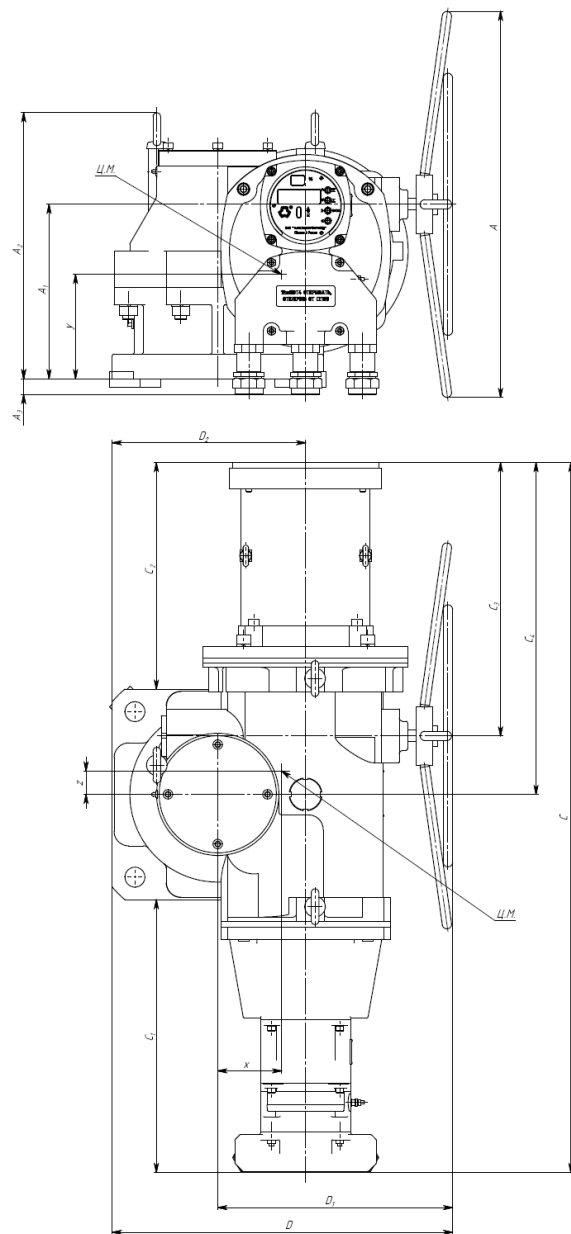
в – Габаритные размеры привода конструктивной схемы 43
